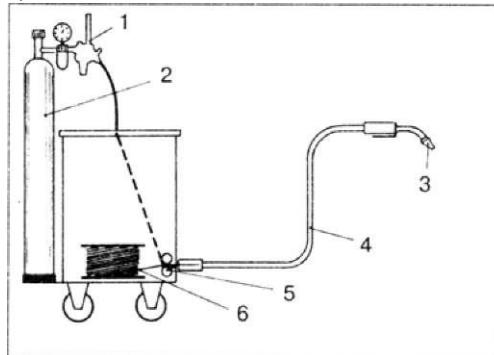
Схема аппарата для сварки в среде защитного газа: 1 - редуктор; 2 - газовый баллон; 3 - горелка; 4 - направляющий шлаг; 5 - механизм подачи проволоки; 6 - катушка с проволочным электродом
